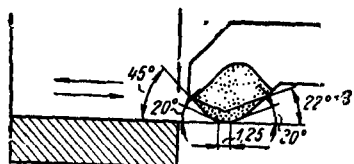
Комбинированный резец для двухстороннего растачивания.
